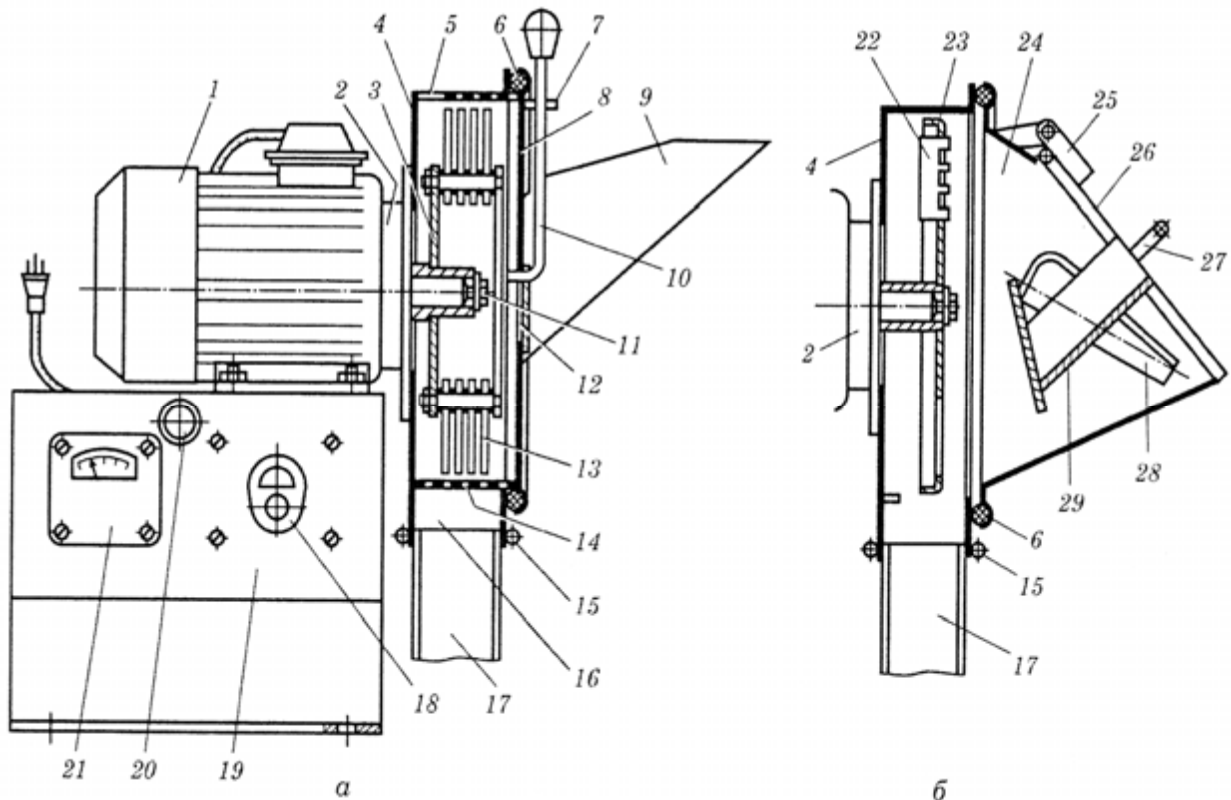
Конструкційні схеми подрібнювач зі змінними робочими органами для переробки зерна (а) та коренеплодів (б):
